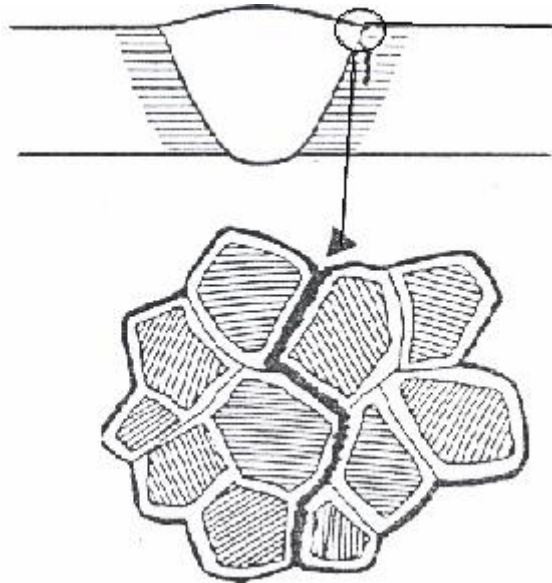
Fissuration du joint de liaison (d'après [10])
